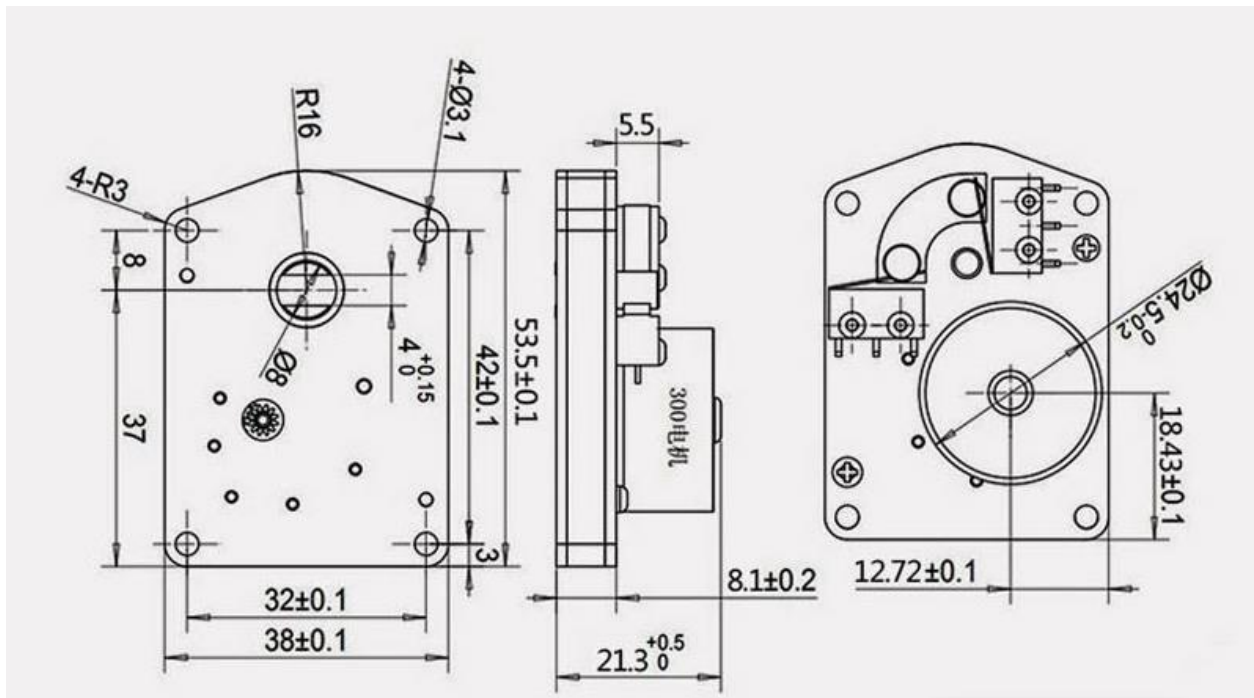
Розміщення елементів щіткового двигуна-редуктора постійного струму
